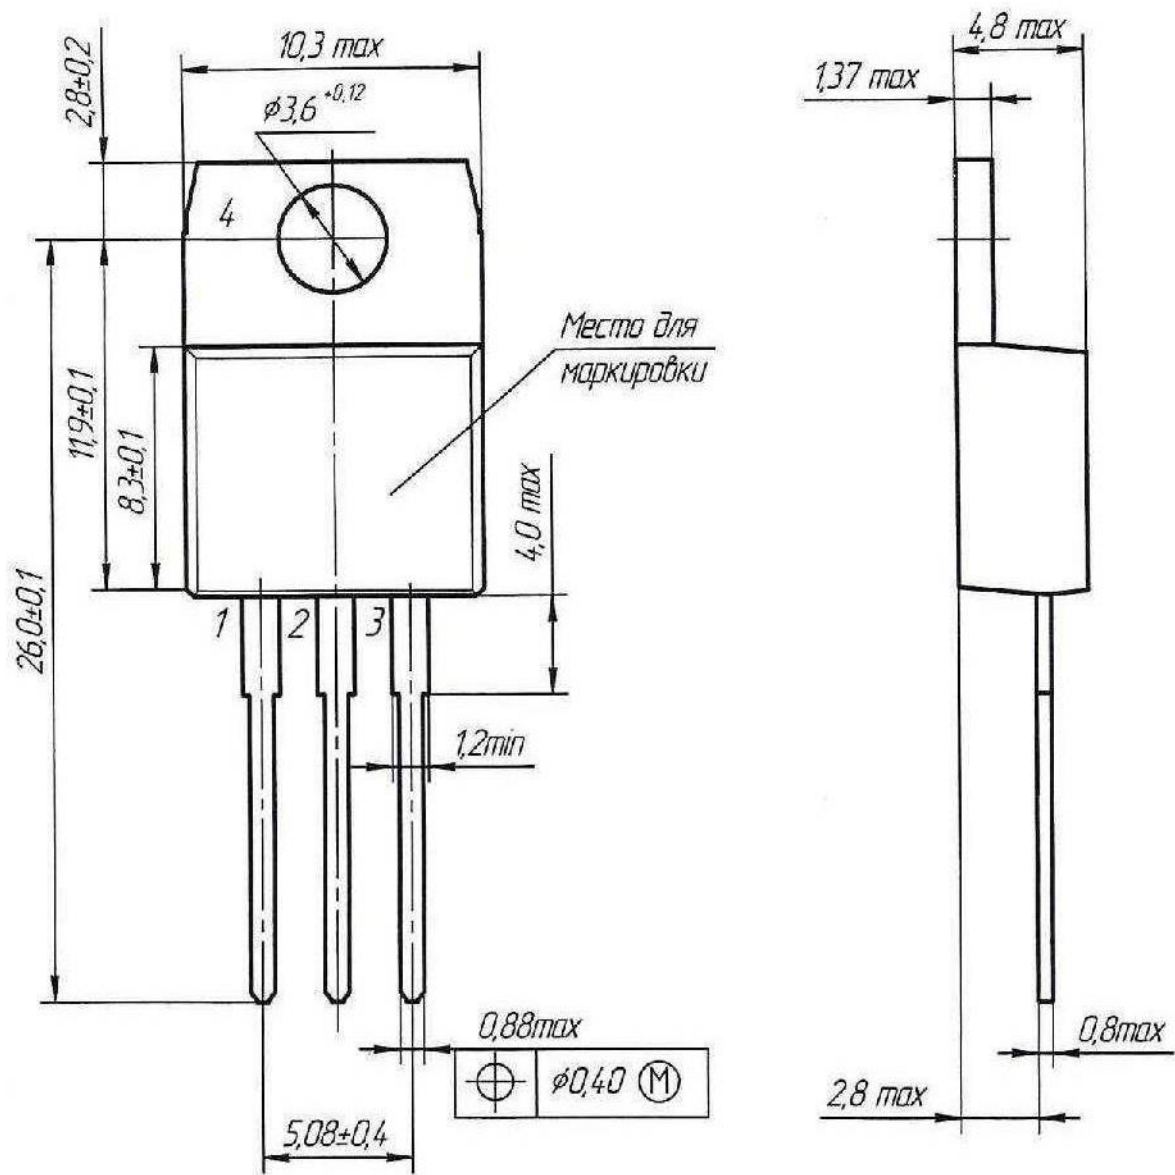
Габаритный чертеж корпуса КТ-28-2.02 (ДФЛК.430209.009ГЧ)
